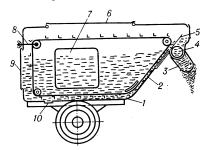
Мобильный раздатчик кормов: 1— бункер; 2— выгрузной транспортёр; 3— скатный лоток раздаточного шнека; у — скатный логок раздаточного шнека,
